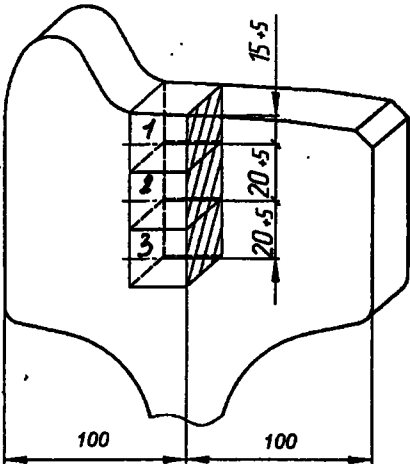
Положение шлифов на поперечном темплете обода цельнокатаного колеса для контроля загрязненности металла колес неметаллическими включениями
